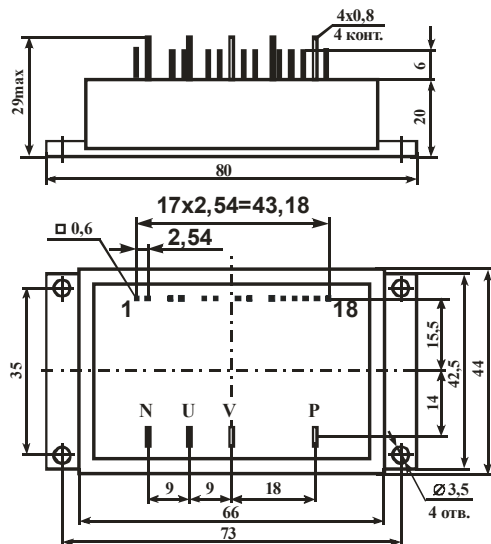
Габаритный чертеж модулей M13MB-10-6
